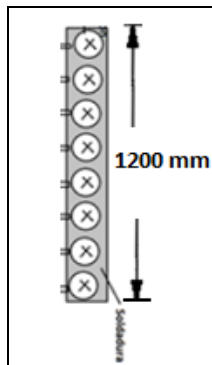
DIMENSIONAMIENTO DEL CORDÓN DE SOLDADURA EN LOS ÁNGULOS.
